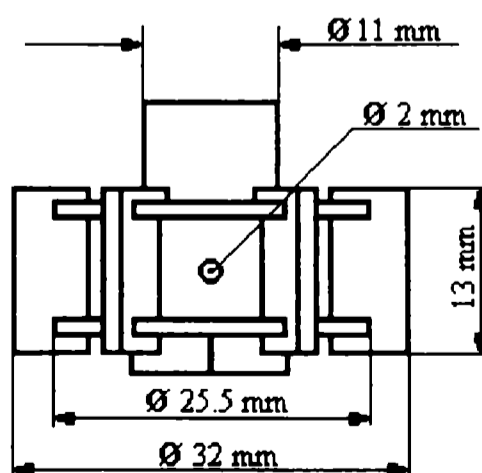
Vista frontal de la turbina de impulsión, dimensiones principales.
